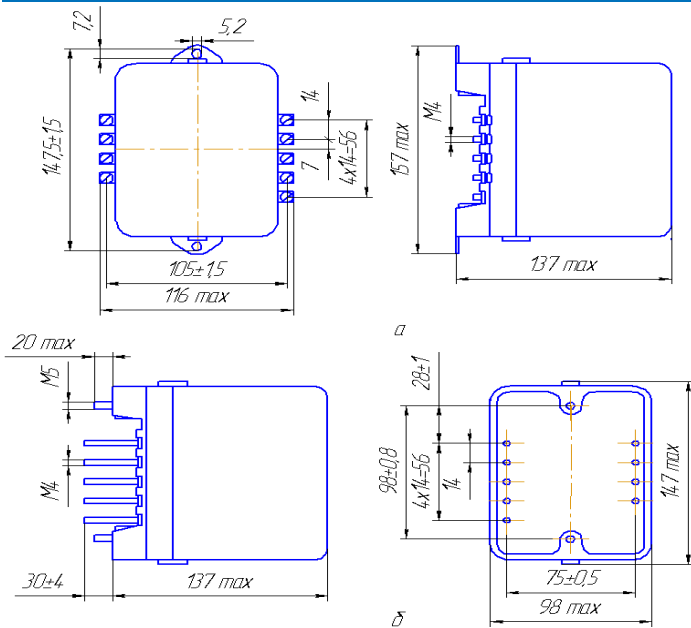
Габаритные, установочные и присоединительные размеры реле типов PB 100, PB 200
